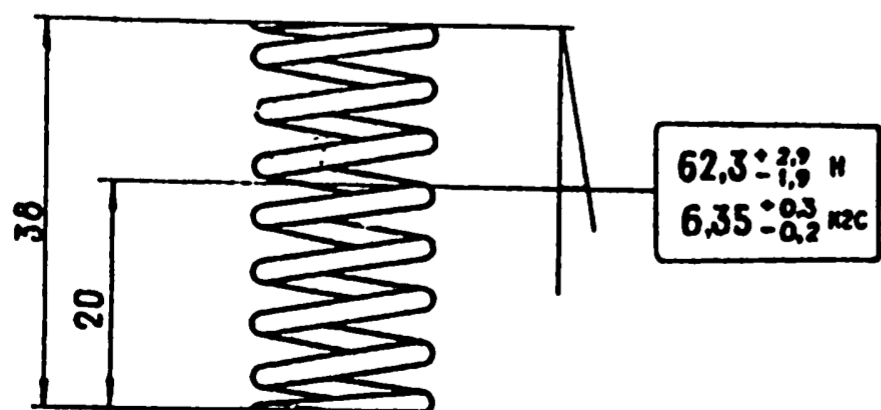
Основные данные для проверки пружины редукционного клапана
